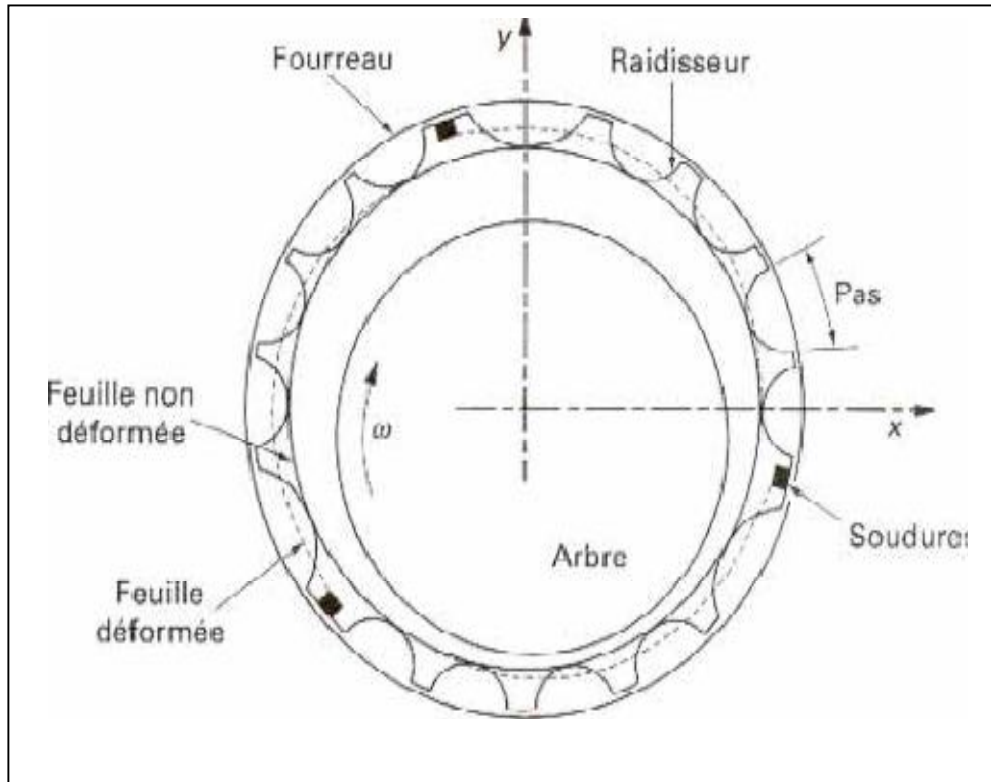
Paliers à 3 feuilles montées sur raidisseurs
